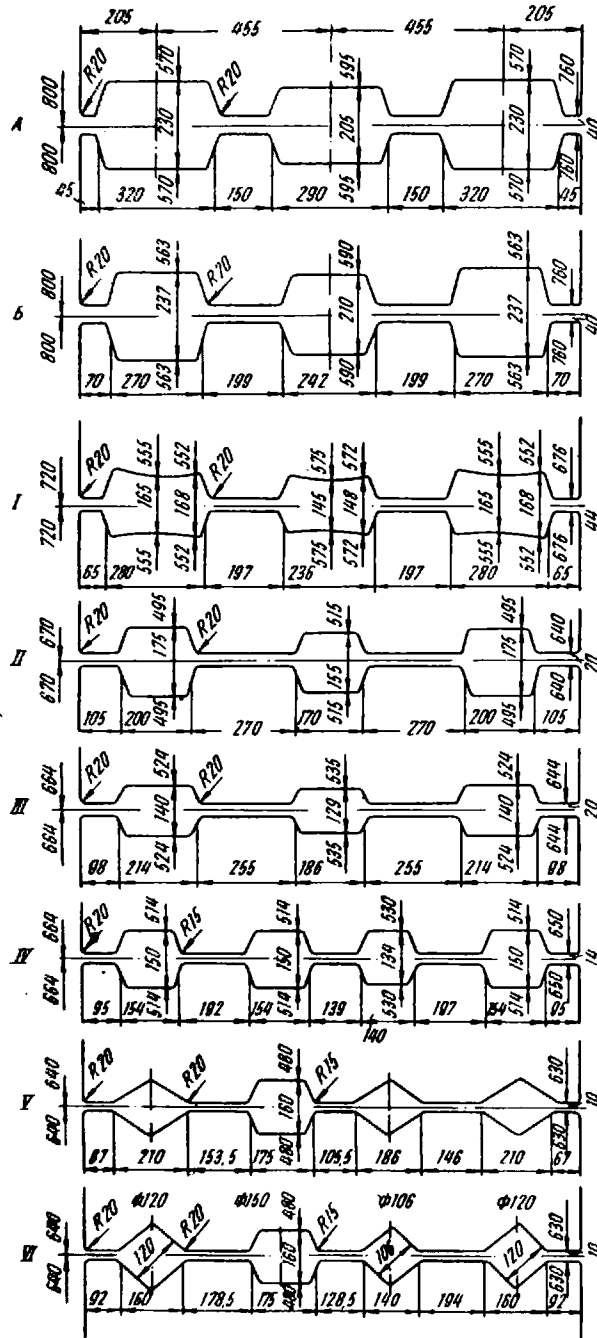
Калибровка валков первой группы клетей непрерывного заготовочного стана 800/630/450
